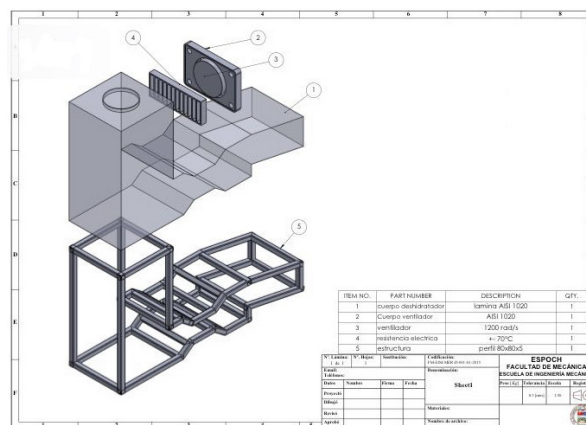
Vista del diseño del Deshidratador Mixto Indirecto de Frutas (DMI), utilizando la plataforma SolidWorks.
